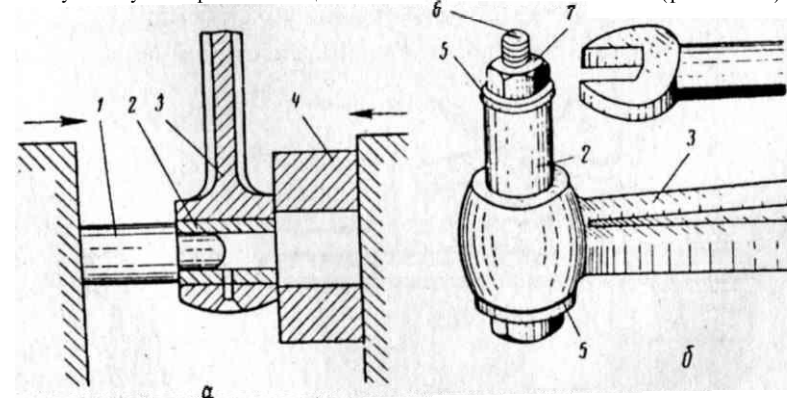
Выпрессовка и запрессовка втулки верхней головки шатуна: а) тисками; б) болтом: 1 - оправка; 2 - бронзовая втулка; 3 - шатун; 4 - вспомогательная втулка; 5 - шайба; 6 - болт; 7 - гайка
